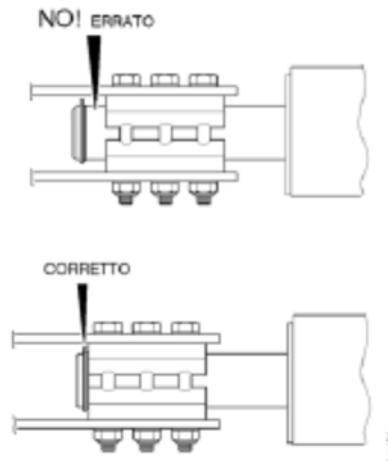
Corretto montaggio dell'anello di sicurezza.
